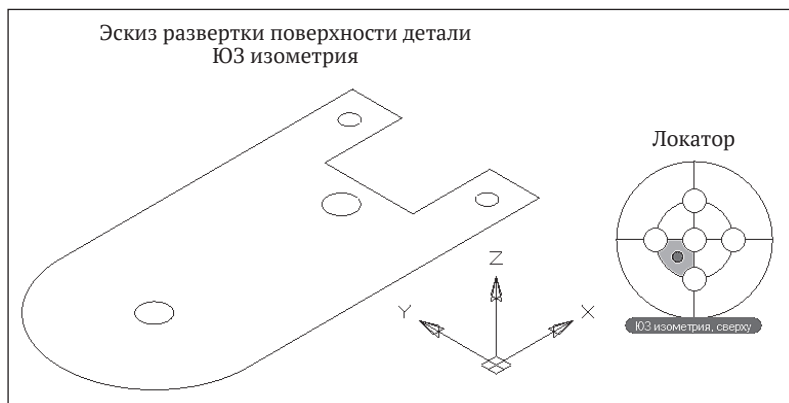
Эскиз развертки поверхности детали «Уголок» в ЮЗ изометрии
